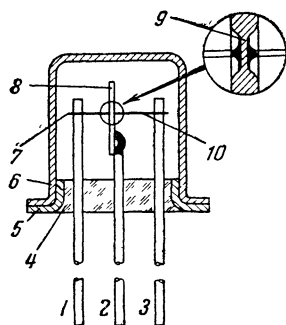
Конструкция поверхностно-барьерного транзистора.
